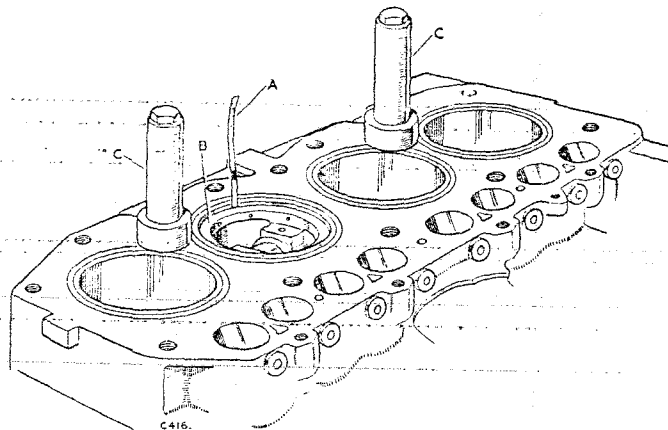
Comprobación de la tolerancia del pistón.
